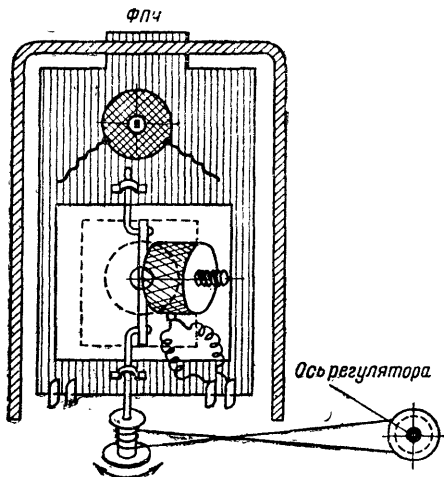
Конструкция ФПЧ с поворачивающейся на 90° катушкой
